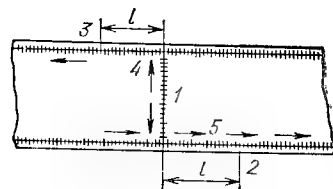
Порядок сварки стыка двутавровых балок.
